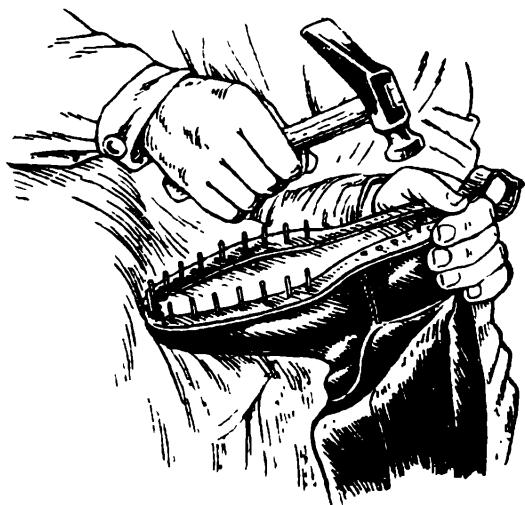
Крепление кругового ранта в пятке деревянными шпильками
